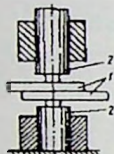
Схема сварки без предварительного зажатия свариваемых деталей.
